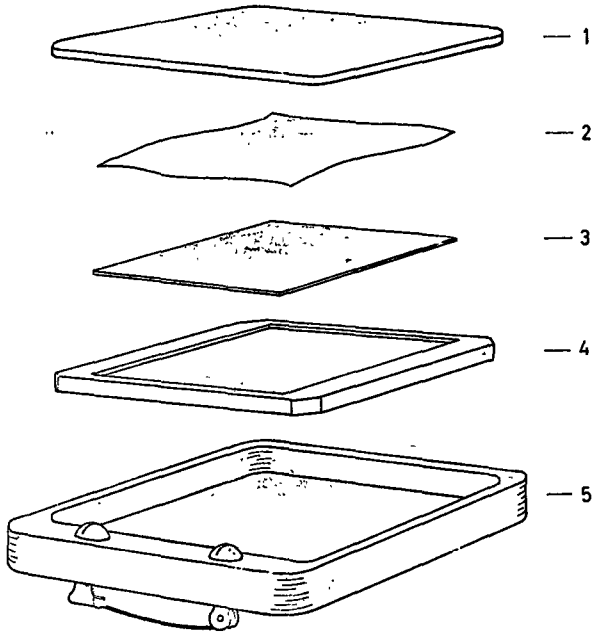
Explosionszeichnung des Spaltfragmentdosimeters
